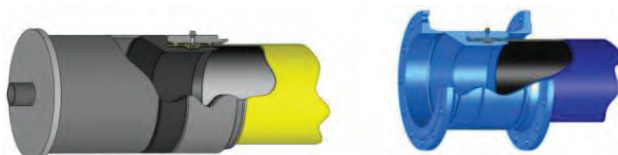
Фланцевый соединитель Примус Лайн [5]
